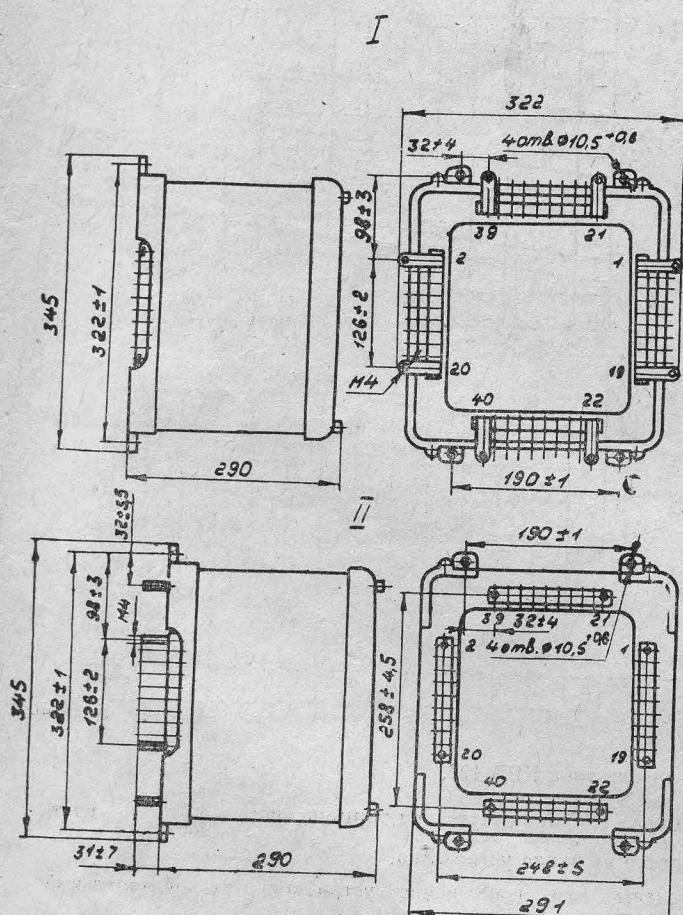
Габаритные и установочные размеры устройства блокировки типа КРБ 126.
